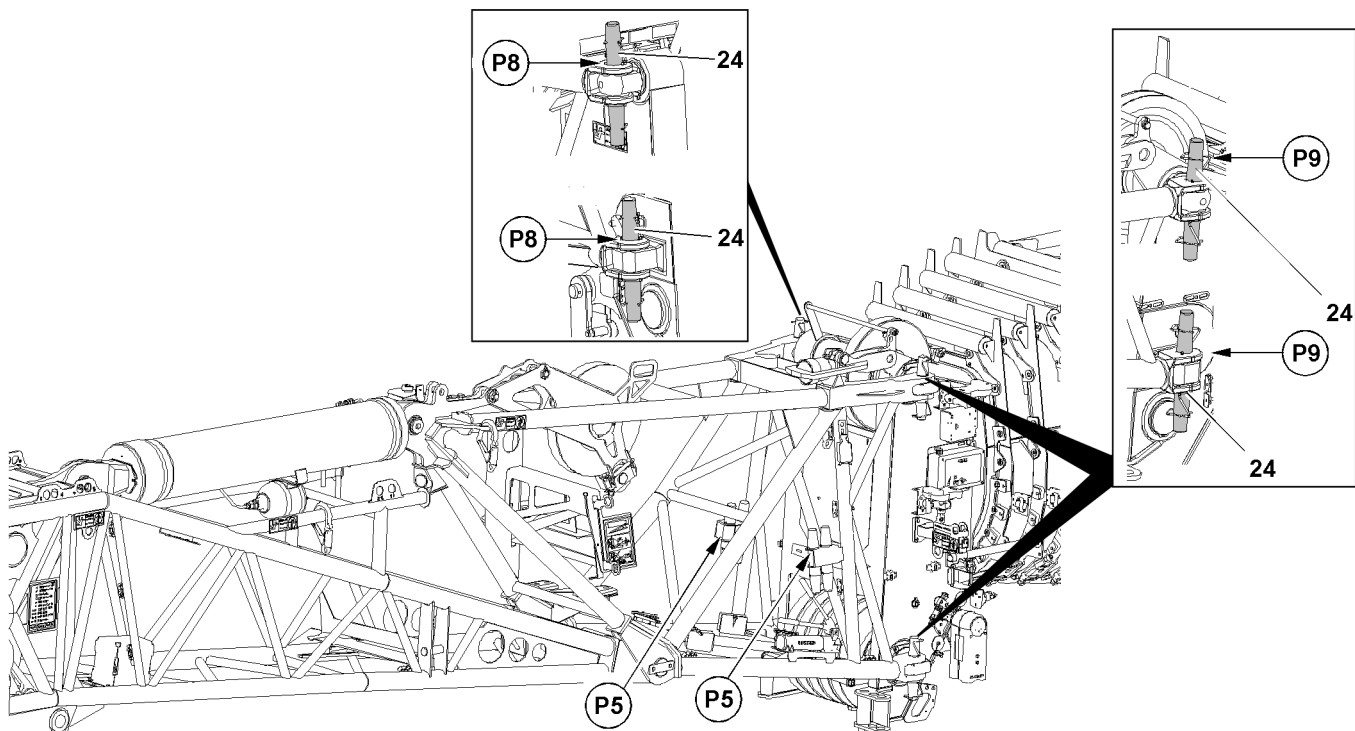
Desmontar o jib rebatível especial transportado separadamente
